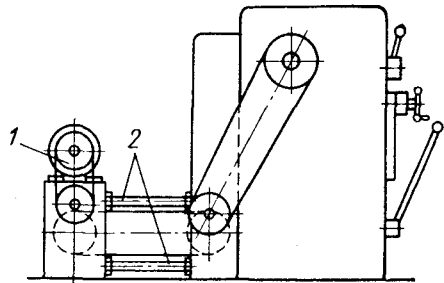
Схема расположения тяг, используемых для уменьшения колебаний станка от двигателя главного привода, расположенного вне станка
